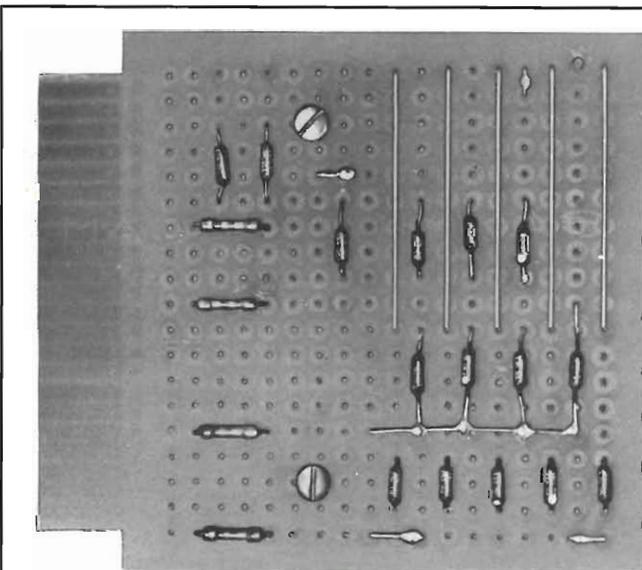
Cablaggio della matrice di fig. 1 visto dal lato dei componenti.
